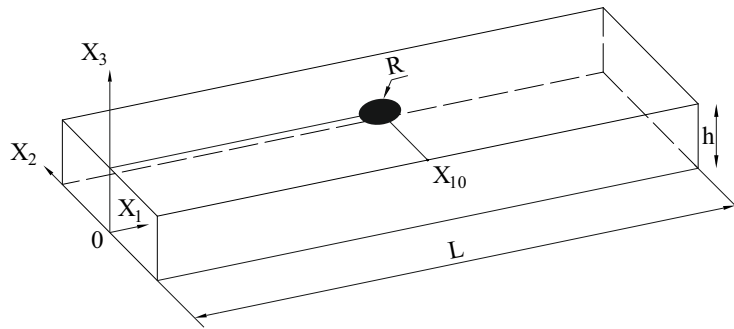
Схема обрабатываемой детали и плоский круглый штамп
